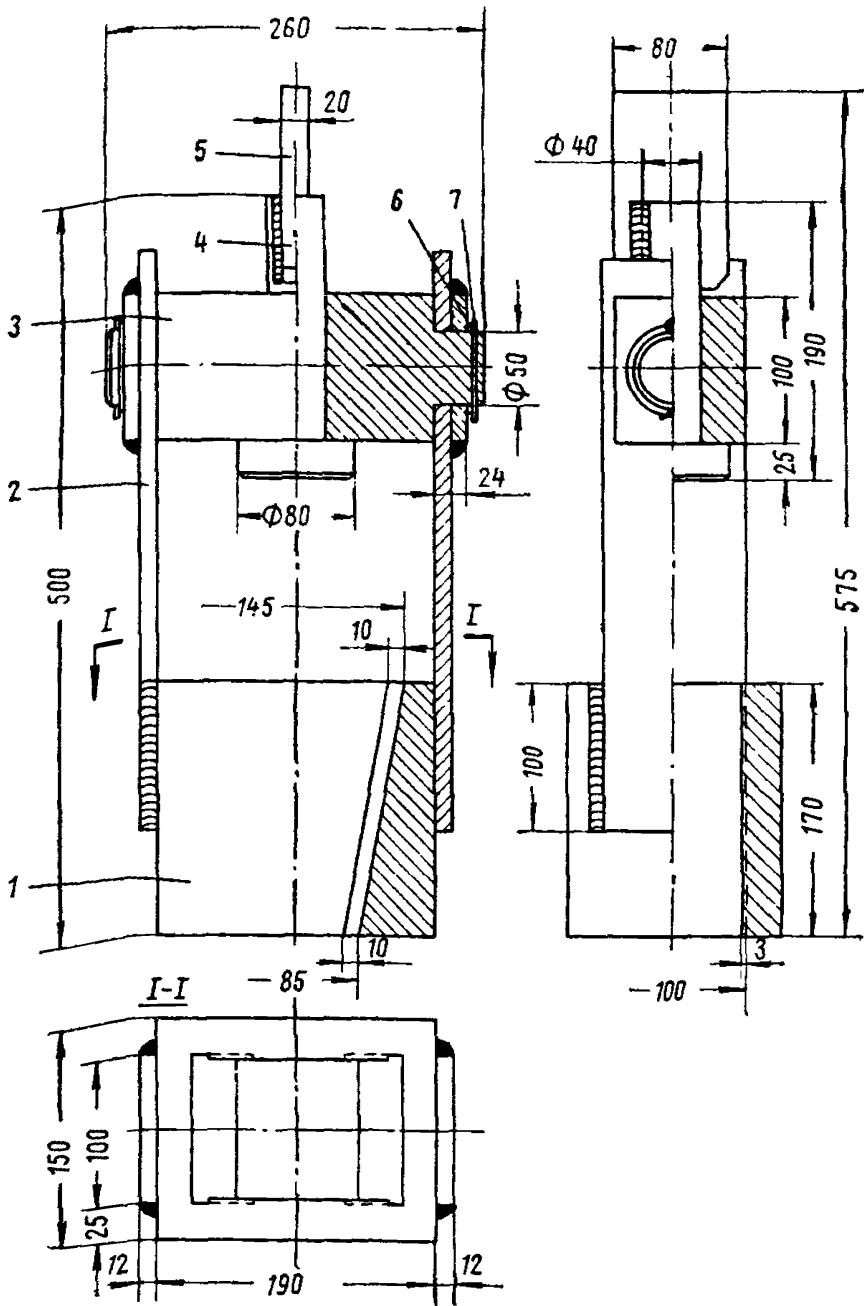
Конструкция силовой рамы для испытания на прочность образцов сварных крестообразных соединений на разрывных машинах типа УММ-50 (ГМС-50)
